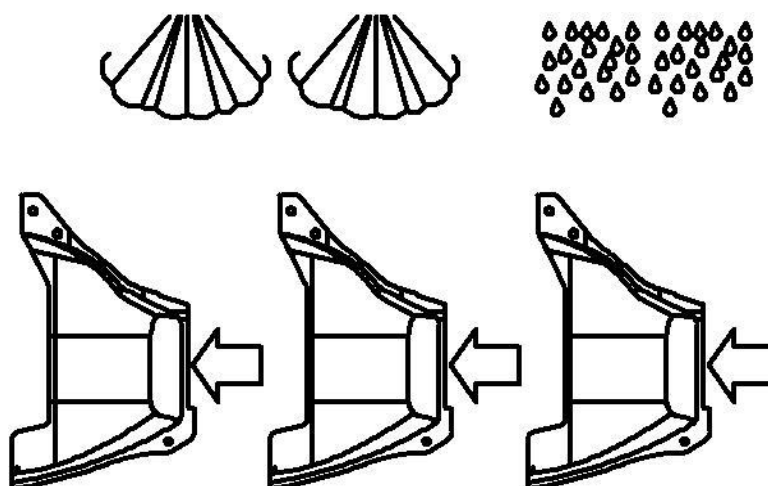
Подготовка деталей к сварке (промывка и просушка)
